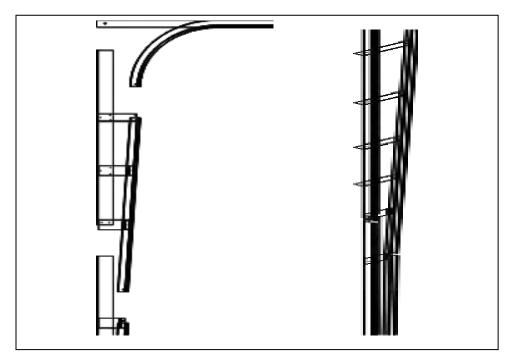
B Montaje de las guías horizontales y Platina TIPO PB2 (High Lift)
